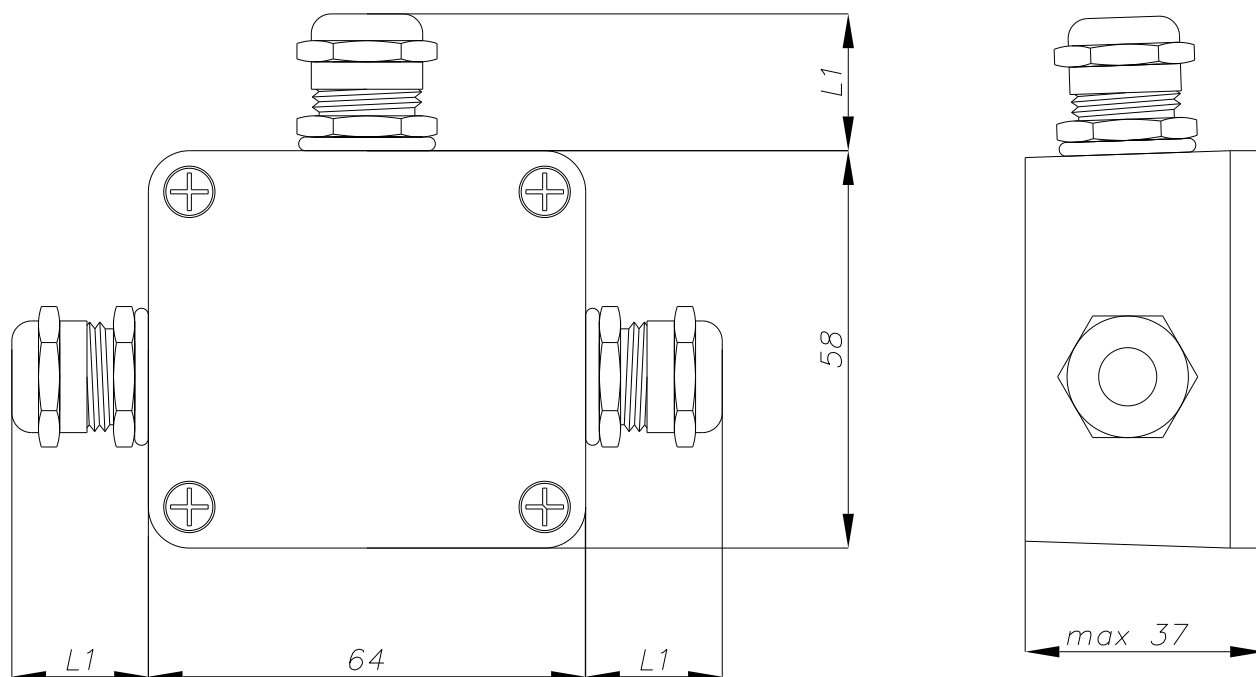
Внешний вид и габаритные размеры разветвителя РПМ-3.
